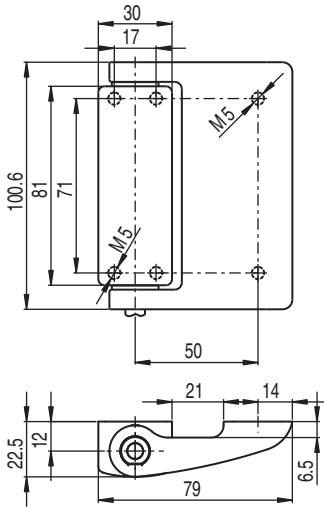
Dimensiones S410-M1CB2-B en mm
